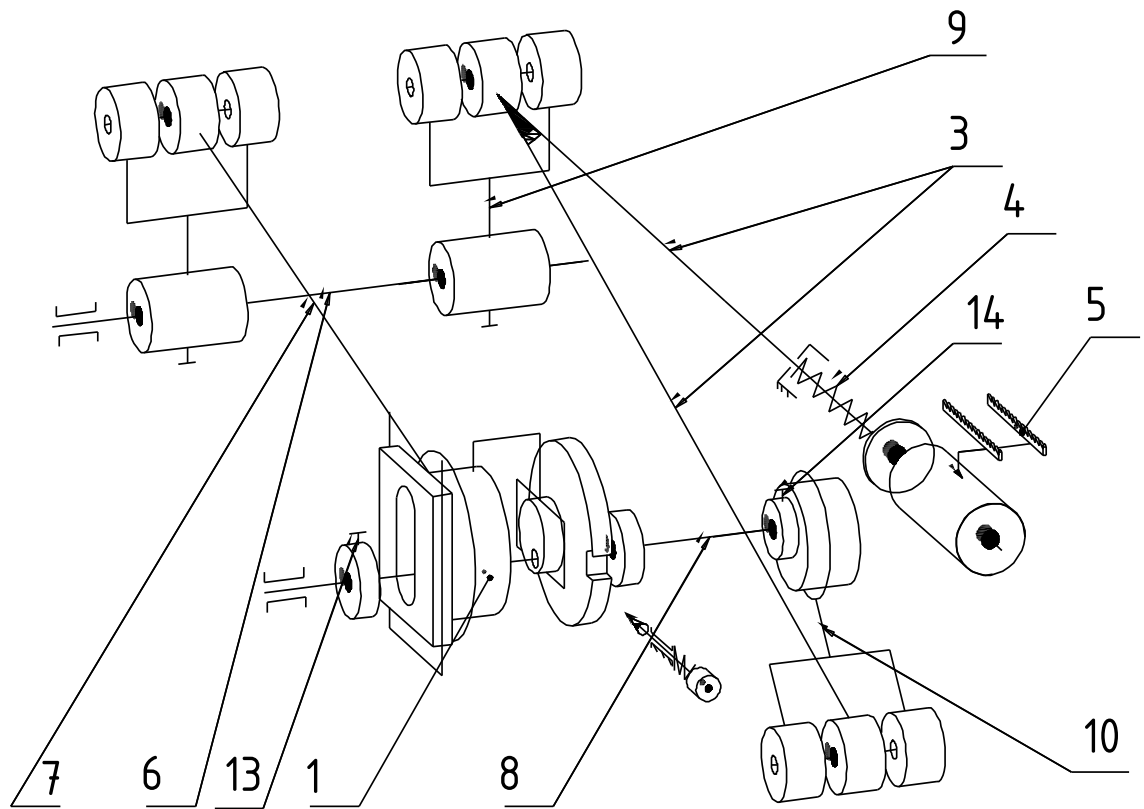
Кінематична схема механізму зубчатої рейки машини 1776 кл. ПМЗ
